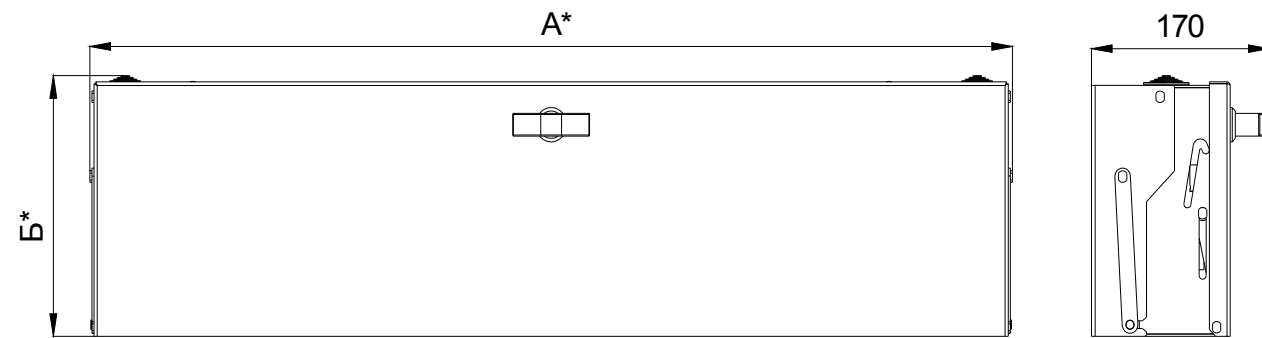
Цоколь для ВЗУ-ЭЦС-Е. Габаритные размеры:
